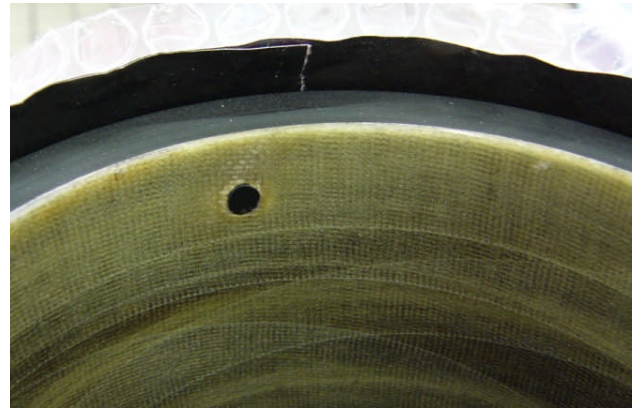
Typischer Kontaktpunkt auf der Innenseite des Presseur-Sleeves
